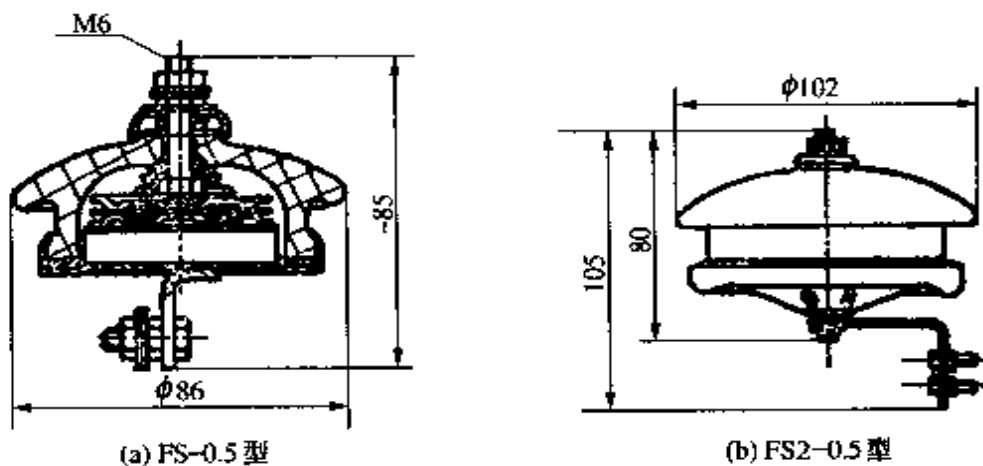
FS-0.5、FS2-0.5 型低压阀式避雷器外形及安装尺寸
